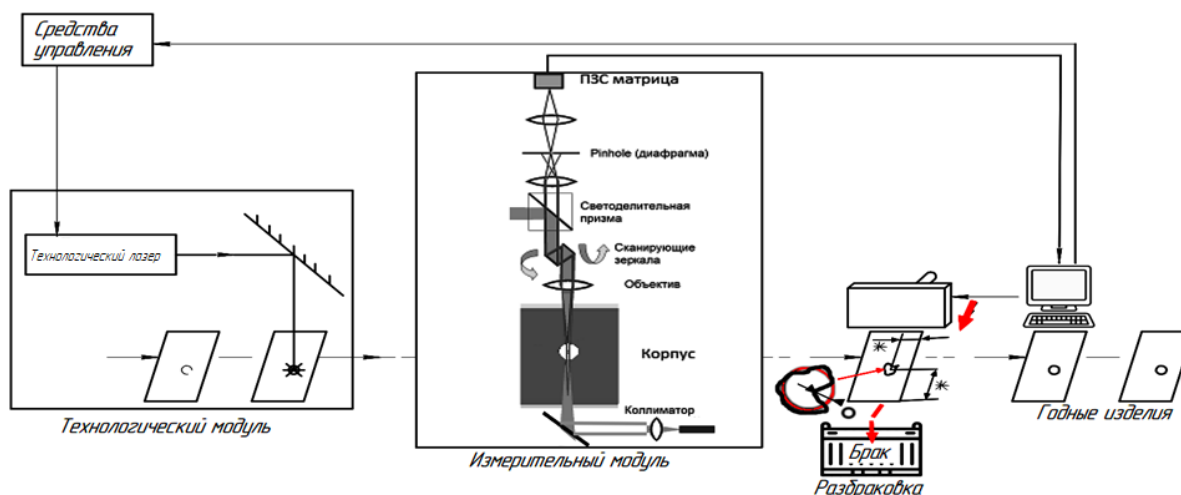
Схема участка линии автоматизированного изготовления и контроля отверстий в корпусах
